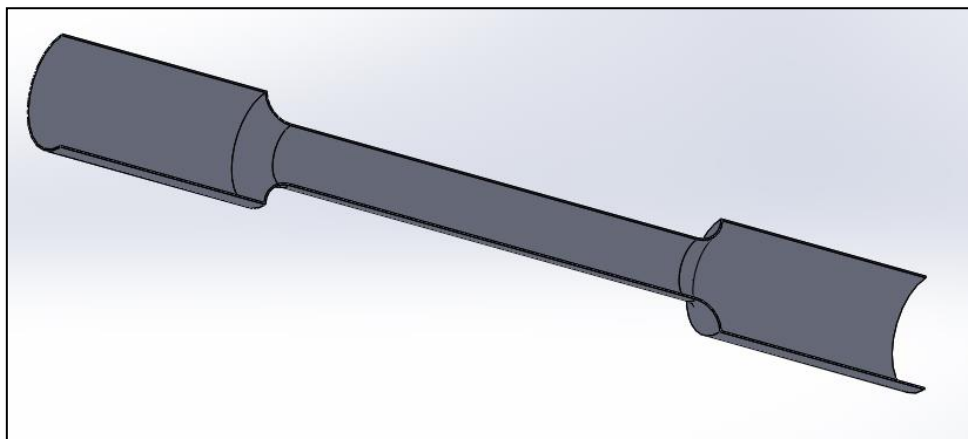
Vue en coupe du revêtement de la première éprouvette
